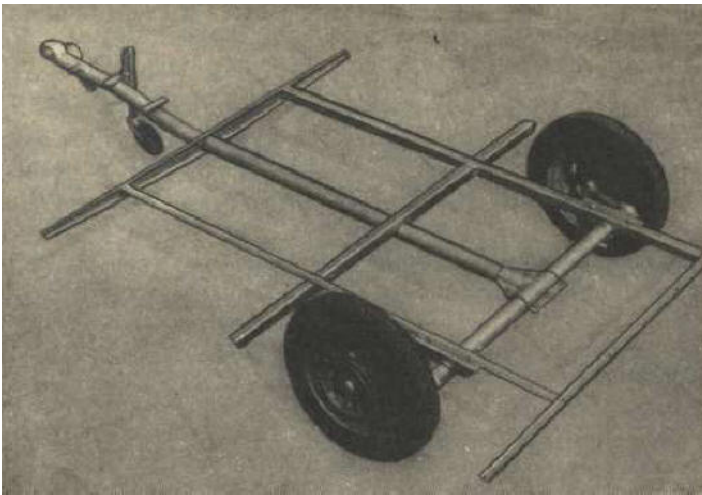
Mittelträgerrahmen mit Torsionsstabachse, ungebremstes Fahrgestell des Campinganhängers Friedel
